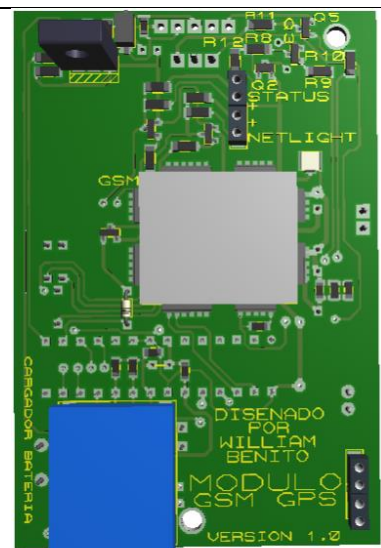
Bottom view 3D del circuito impreso módulo alarma
